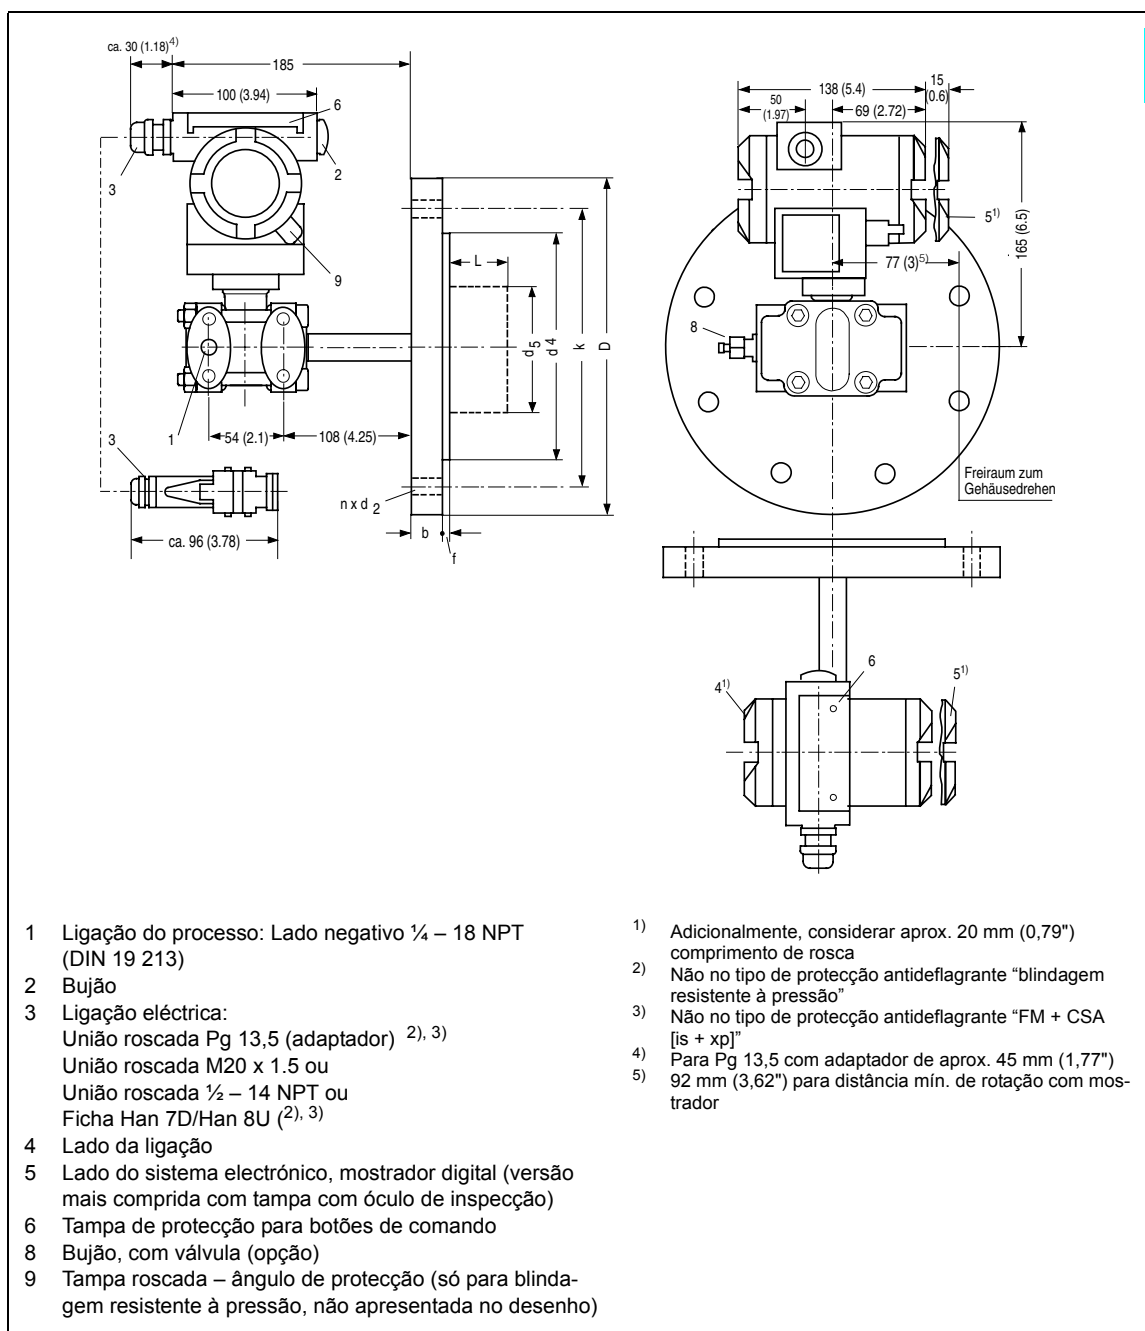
Série DS III para nível (transmissor com flange de montagem), dimensões em mm (polegadas)
